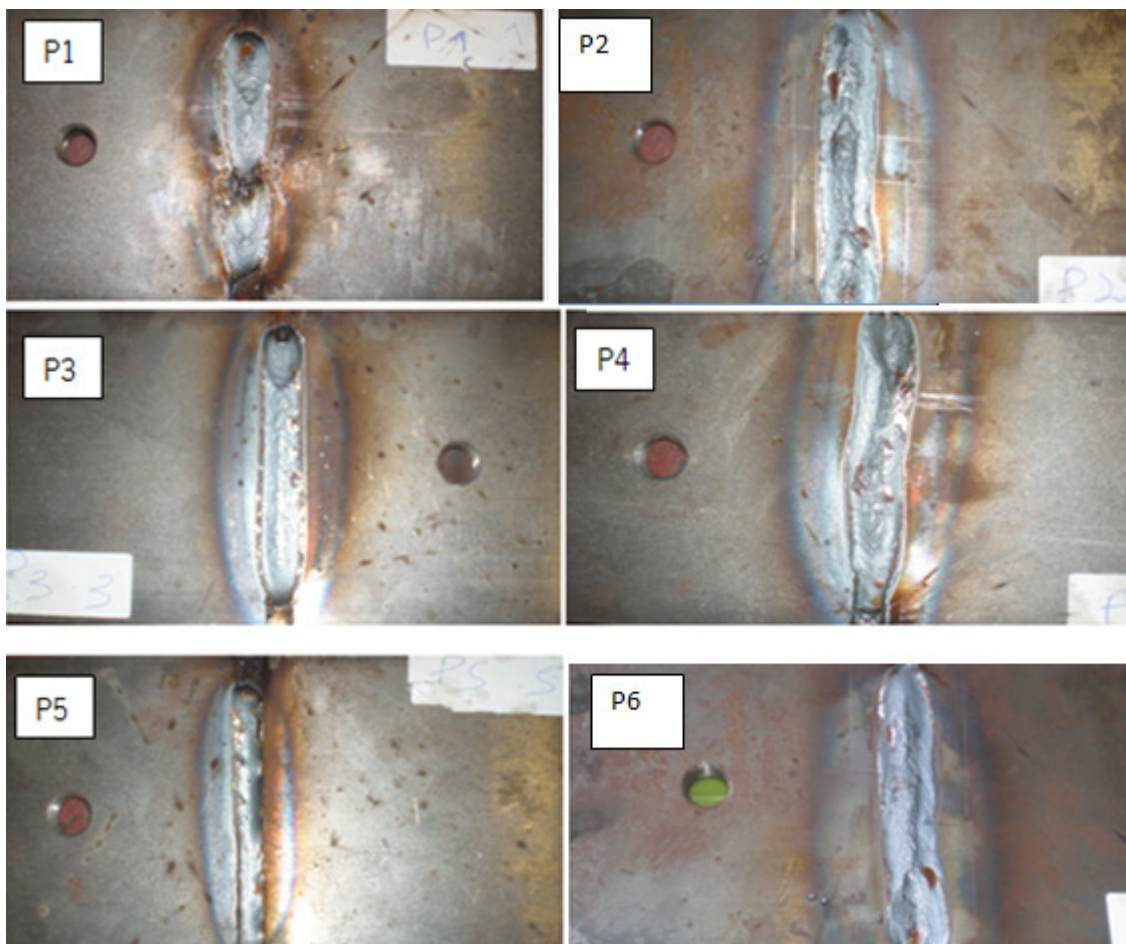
60 - Cordões de soldadura dos provetes.
